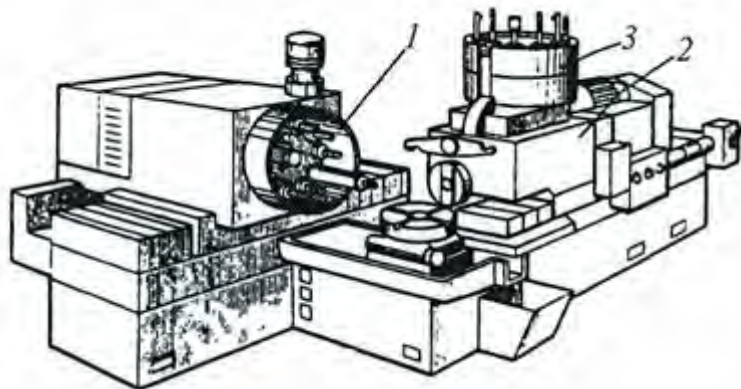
Агрегатний верстат з автоматичною зміною інструменту за програмою
